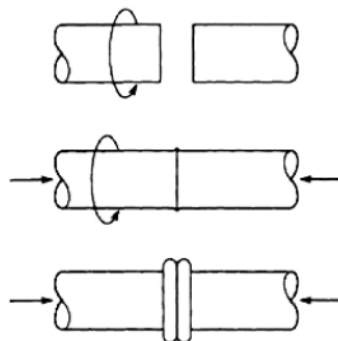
Processo básico de solda por fricção (ASM Handbook).
